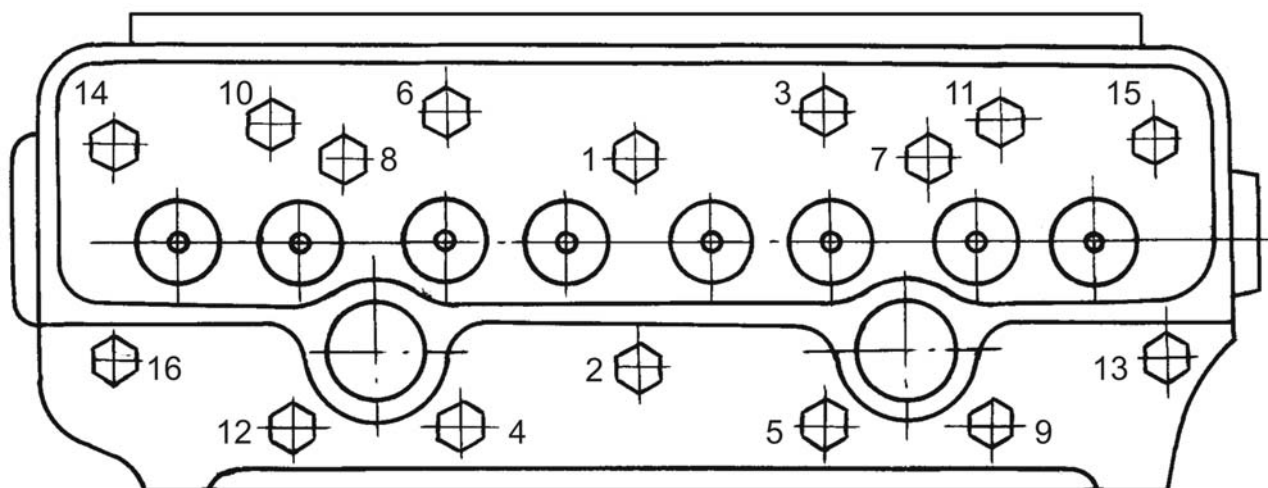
Схема последовательности затяжки болтов крепления головки цилиндров
